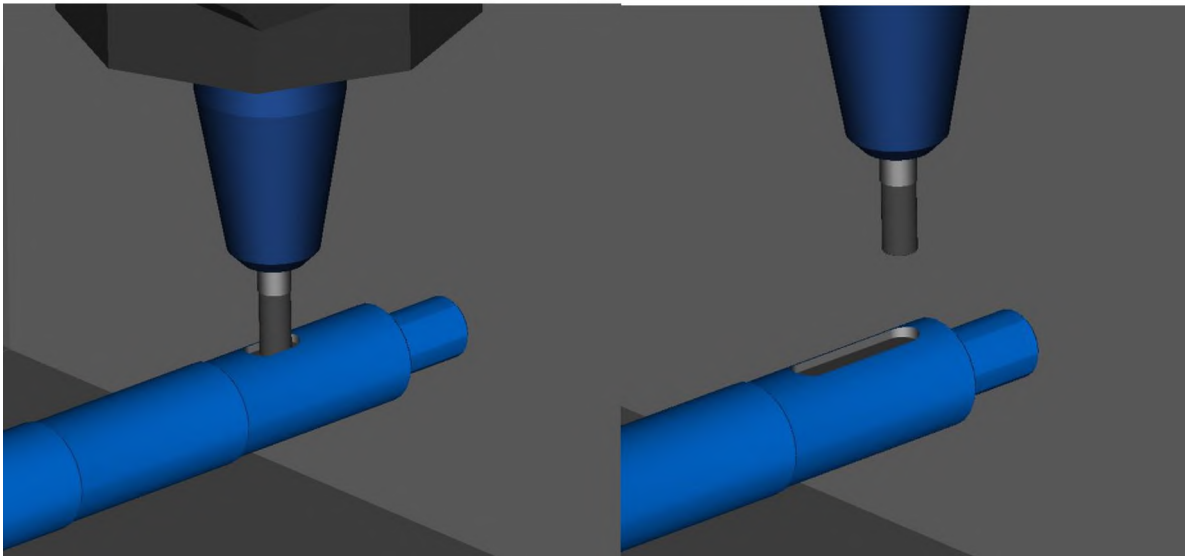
Фрезерування шпонкового пазу кінцевою фрезою
